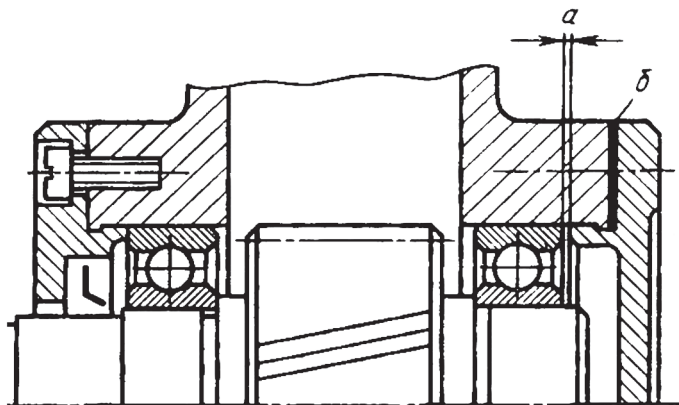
Конструкция сборочной единицы для регулировки зазора
